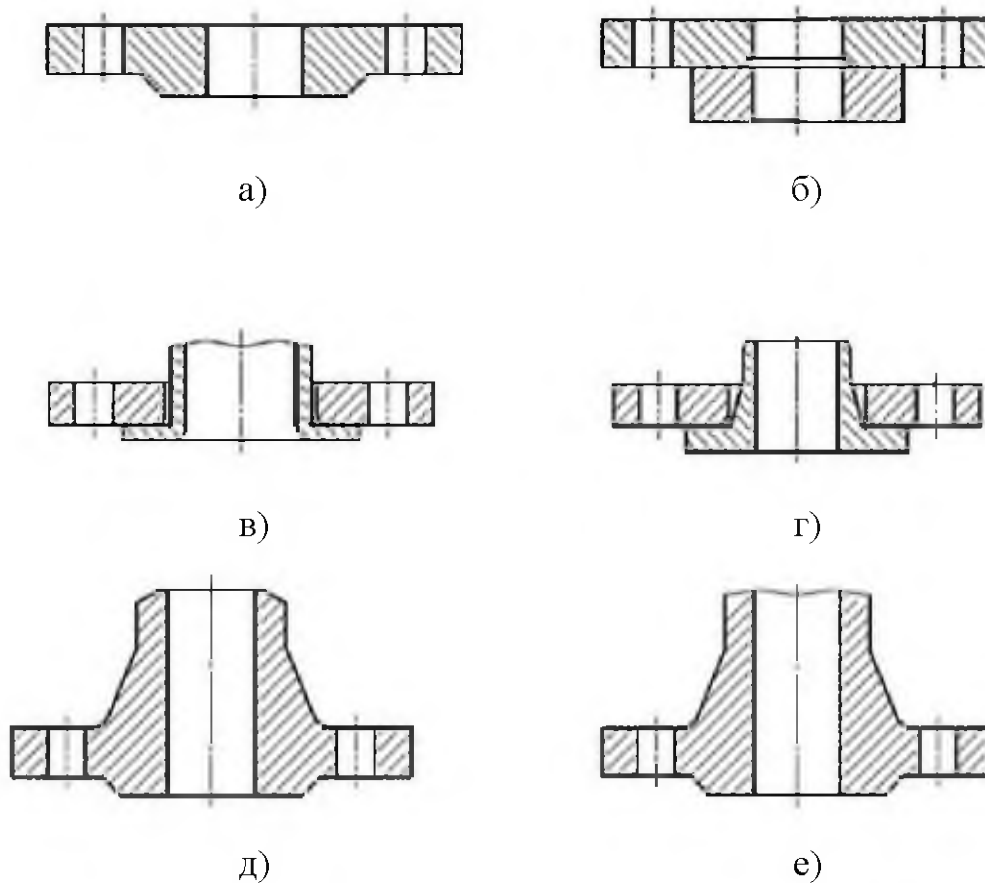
Типи фланців: а) тип 01 – сталевий плоский приварний; тип 02 – на приварному кільці; тип 03 – на відбортуванні; тип 04 – під приварювання; тип 11 – приварний встик; тип 21 – приварний встик;
